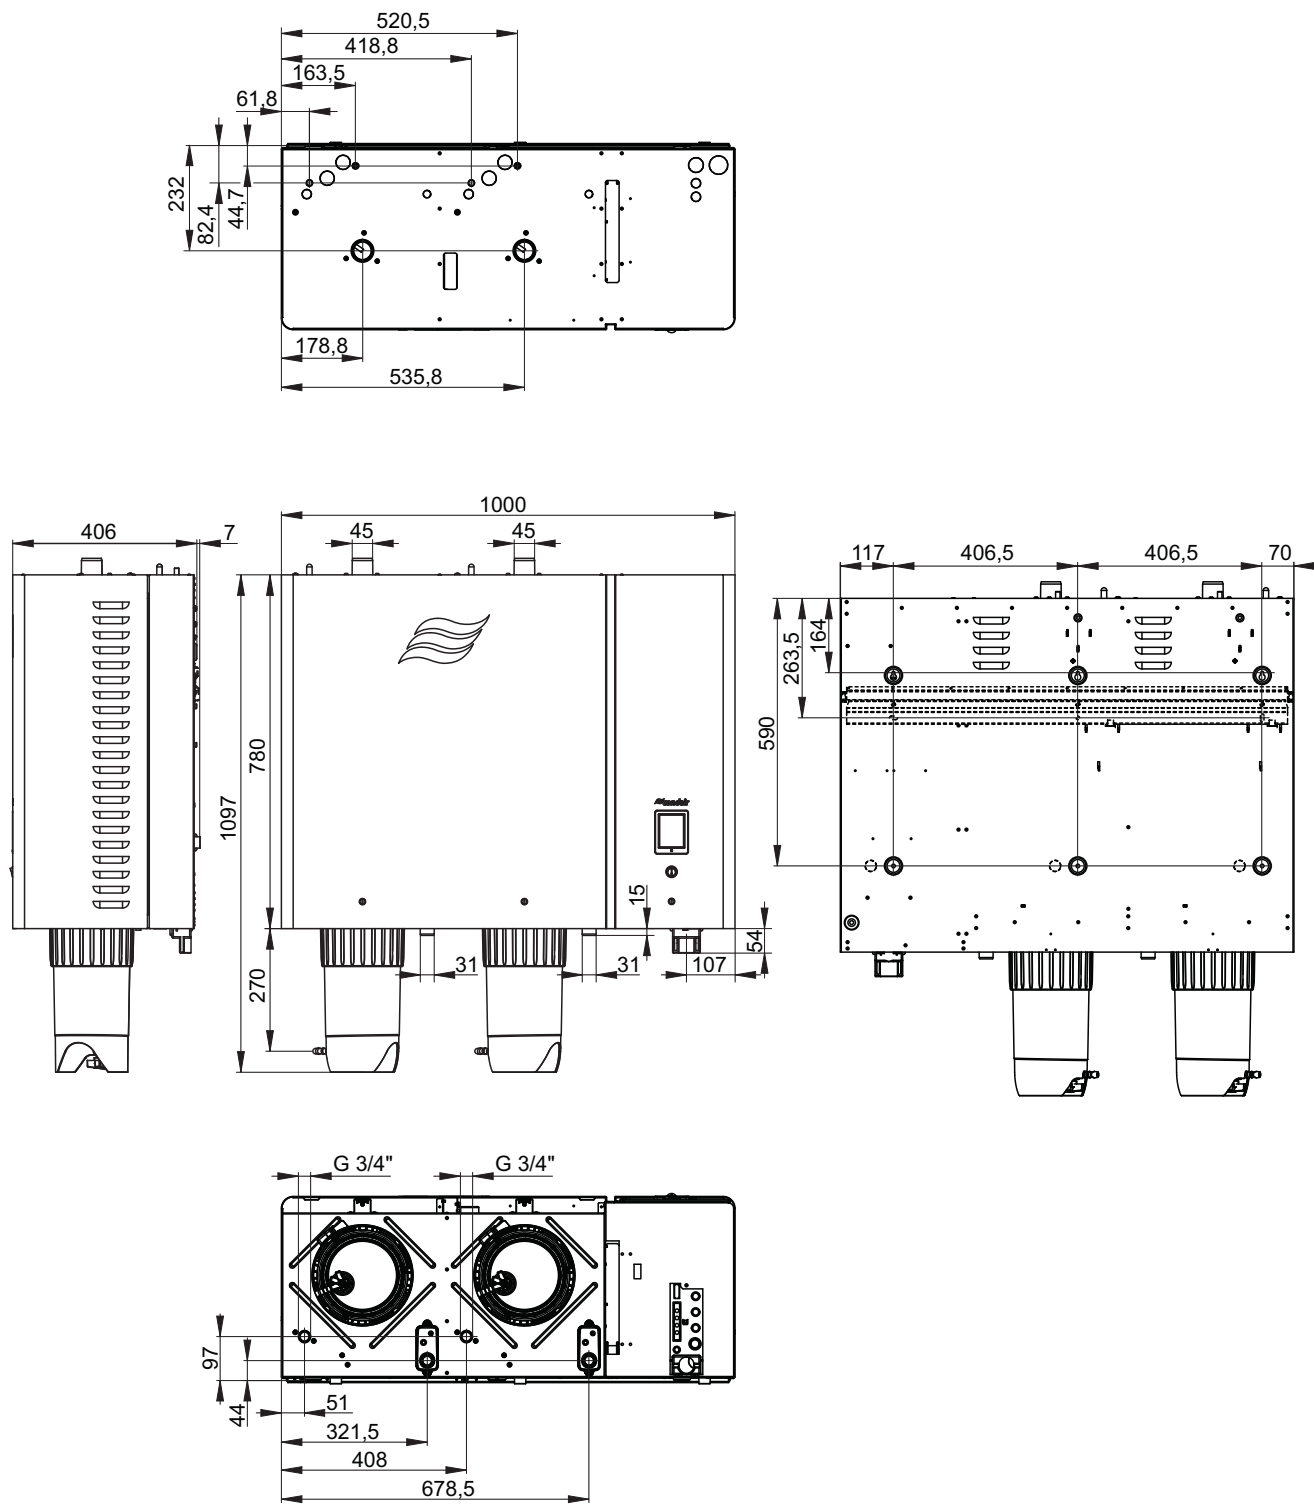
Габаритный чертёж корпуса большого типоразмера (размеры в мм)
